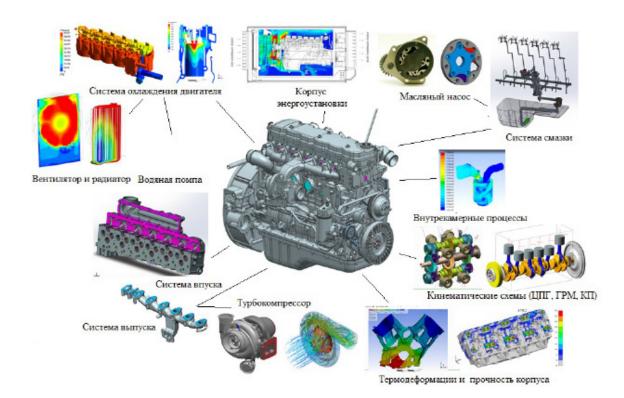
Декомпозиция двигателя газопоршневой энергоустановки
